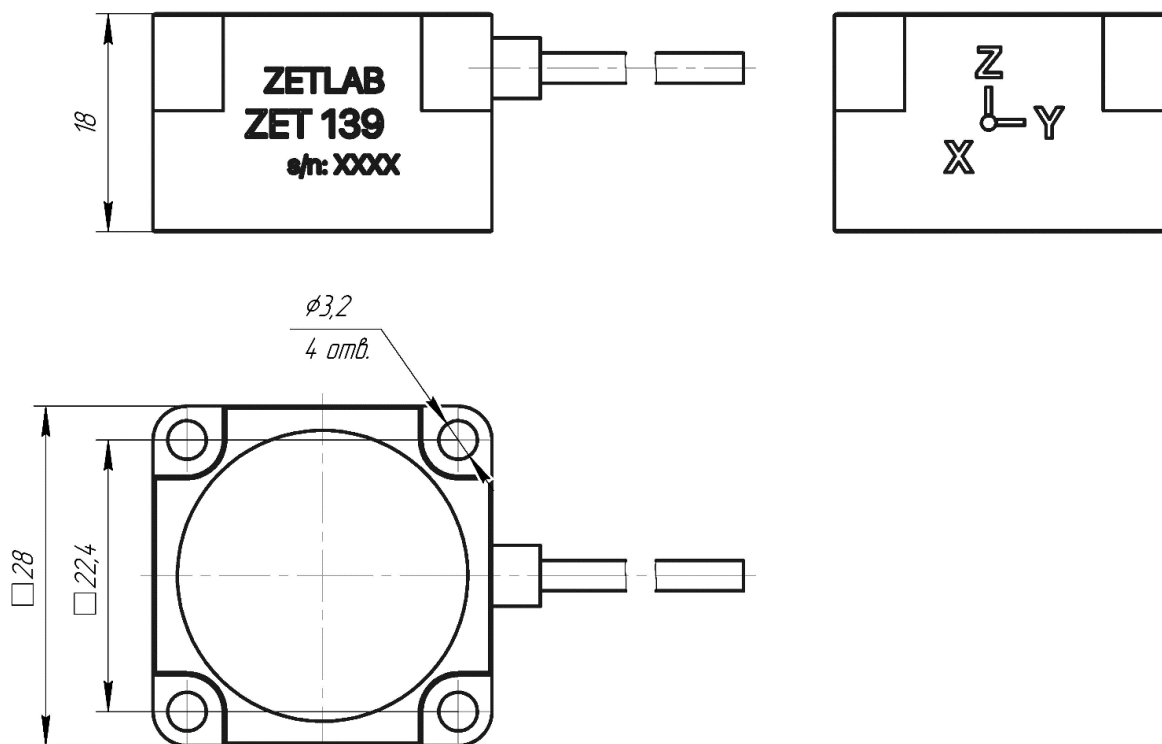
Габаритный чертеж вибропреобразователя ZET 139
